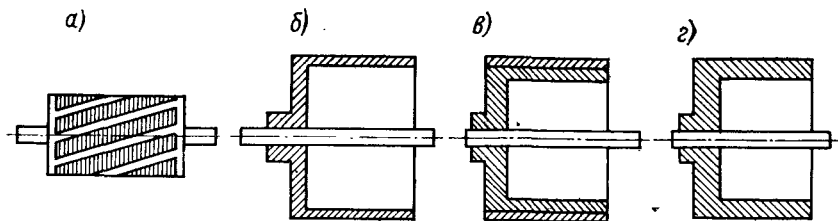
Типы конструкций ротора двухфазного управляемого двигателя: а — «беличья клетка»; б — полый немагнитный ротор; в — ферромагнитный омедненный ротор; г — ферромагнитный ротор
